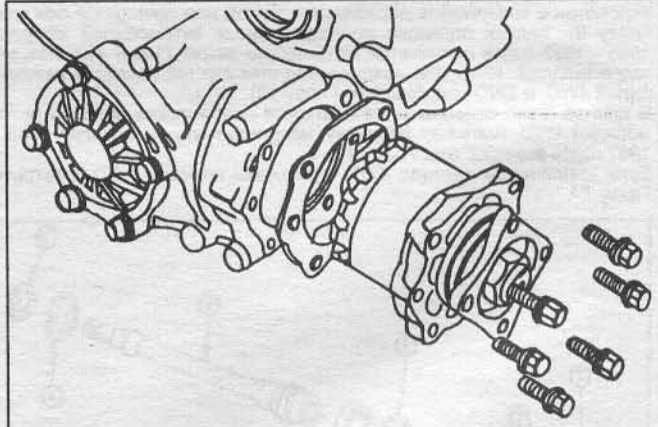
Узел крепления ведомой шестерни к раздаточной коробке.
